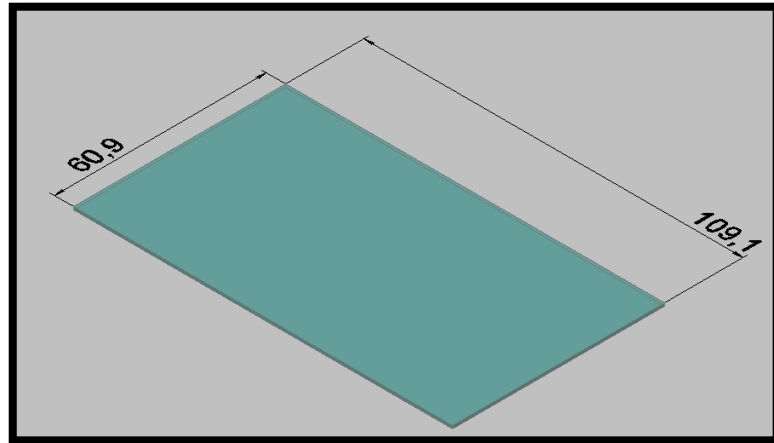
Dimensiones de la pieza No 6.<sup>55</sup>
